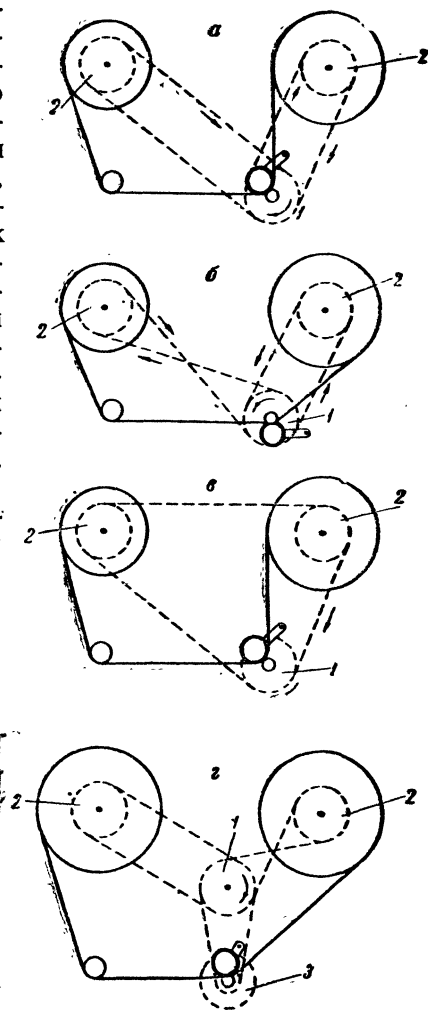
Четыре варианта одномоторной кинематической схемы: 1 — шкив двигателя; 2 — фрикцион; 3 — маховик
